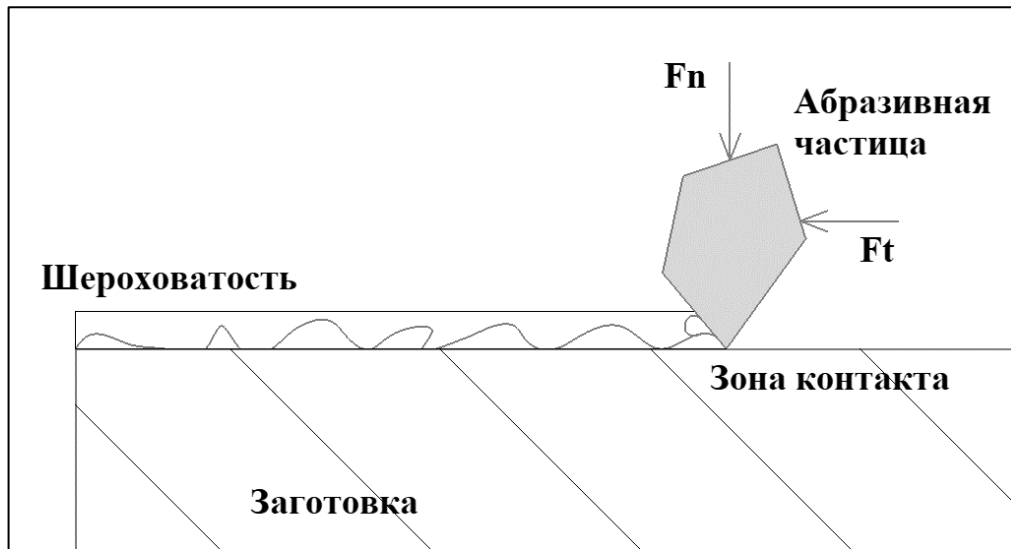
Схема воздействия абразивной частицы на поверхность заготовки, где: F_n – нормальная сила; F_t – тангенциальная сила
